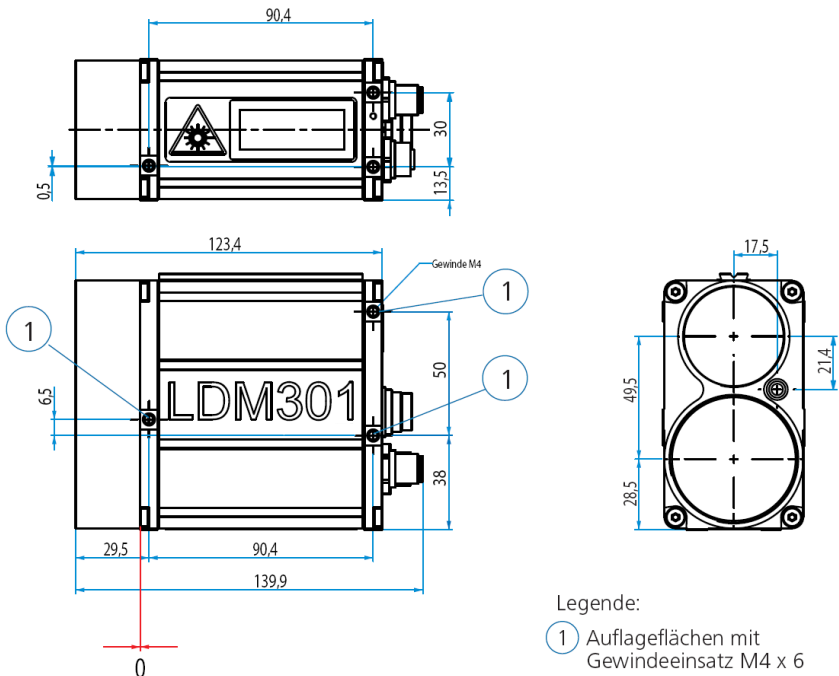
Einbaumaße und Lage des Nullpunktes (Maße in mm)
